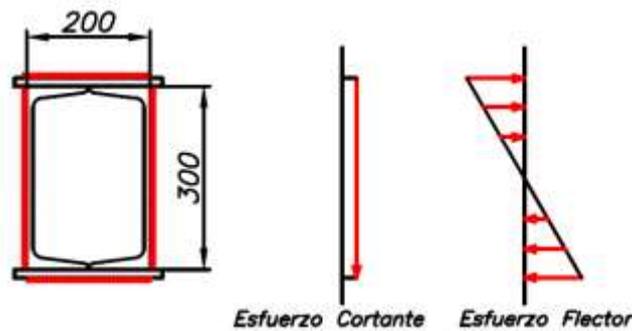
Esfuerzo cortante y flector en soldadura. Fuente: (Autor)
